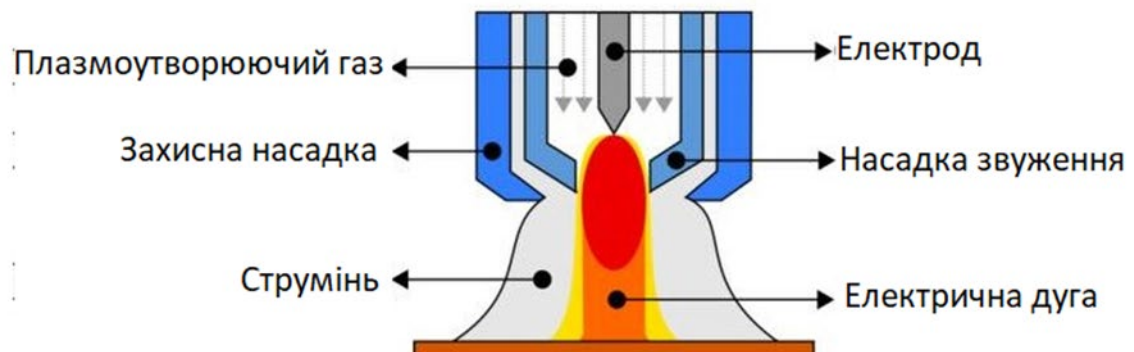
Схема плазмово-дугового наплавлення [15]
